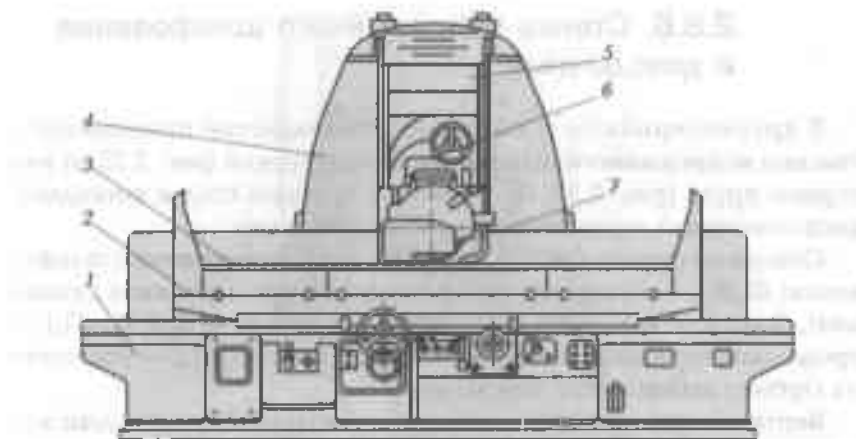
Общий вид плоскошлифовального станка, обрабатывающего детали периферией круга:
